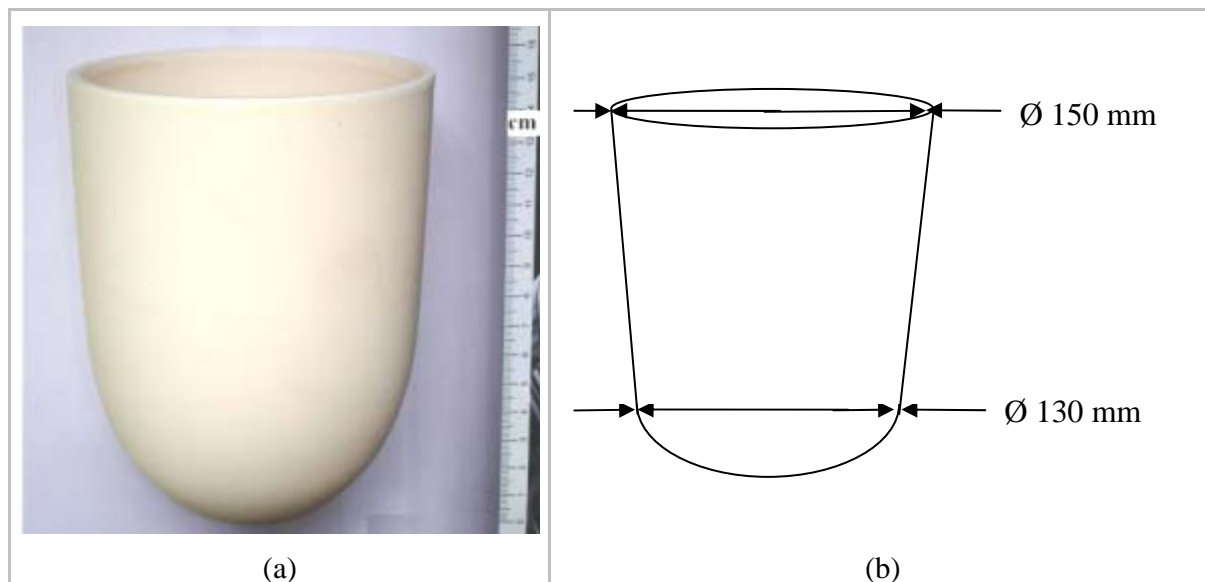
(a) imagem do cadinho de alumina (b) desenho do cadinho representando as suas dimensões.
